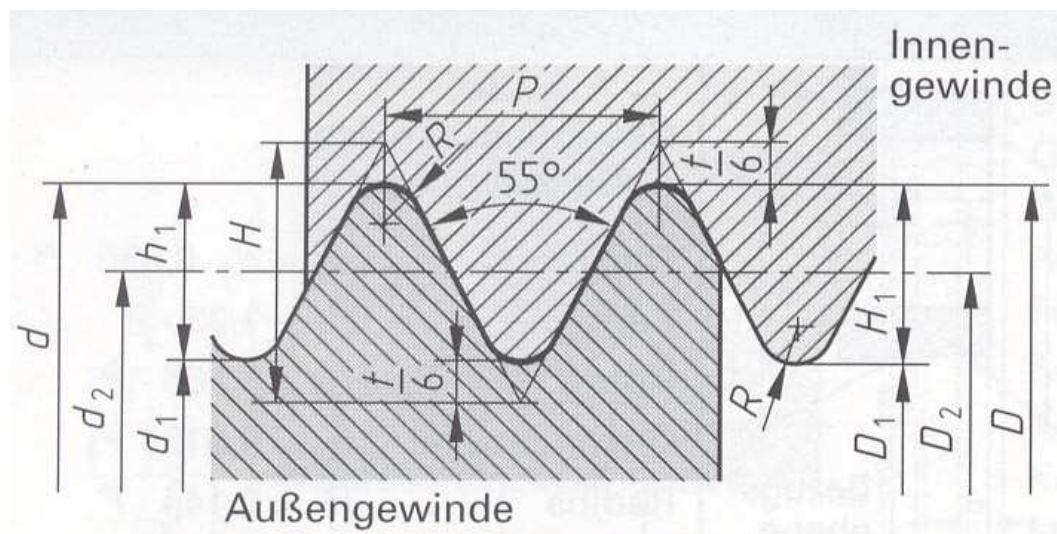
Technische Zeichnung des Whitworth-Gewindes nach DIN 11 (Heinzler *et. al.*, 2002)
